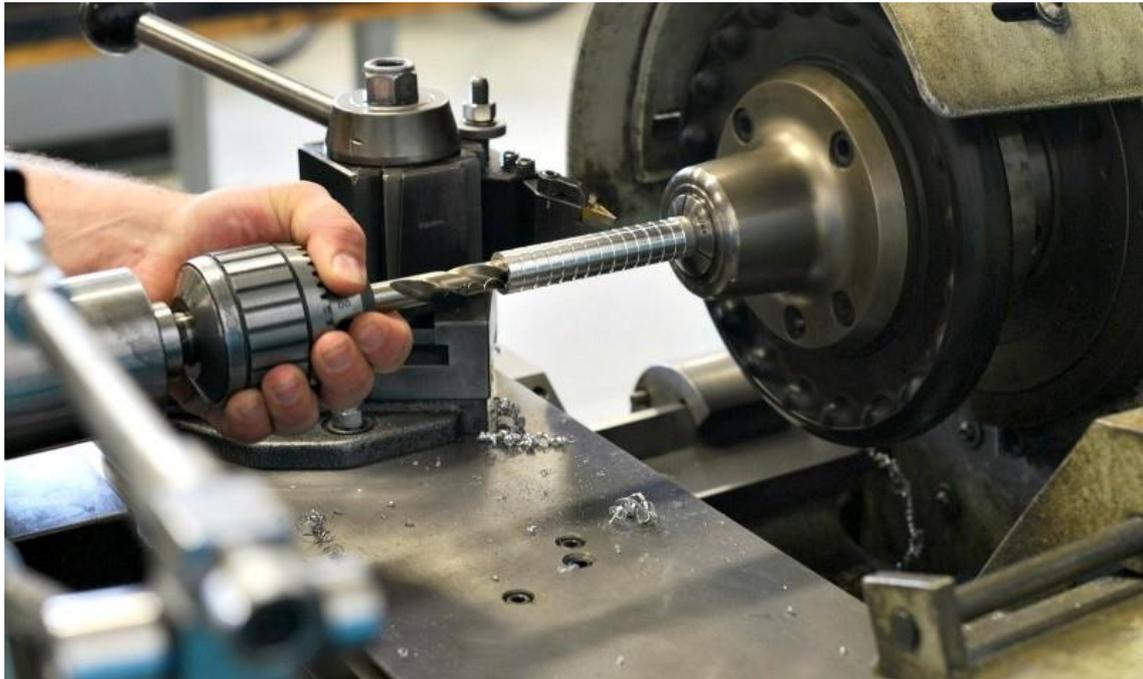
Mecanizado de ejes - Fuente: <https://kuzudecoletaje.es/mecanizado-arranque-viruta/>
